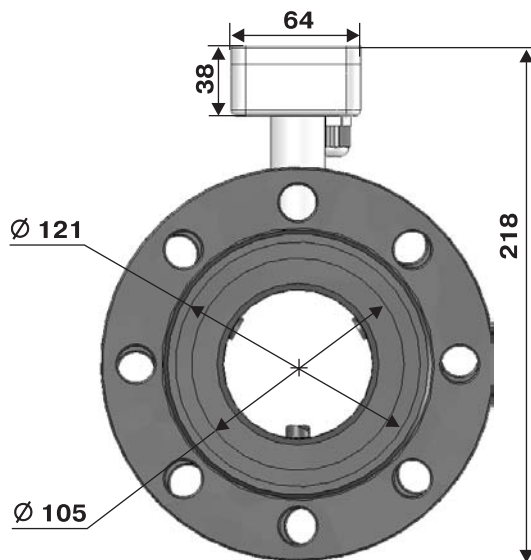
Габаритные и установочные размеры расходомеров ДУ80 (вид спереди и разрез)
